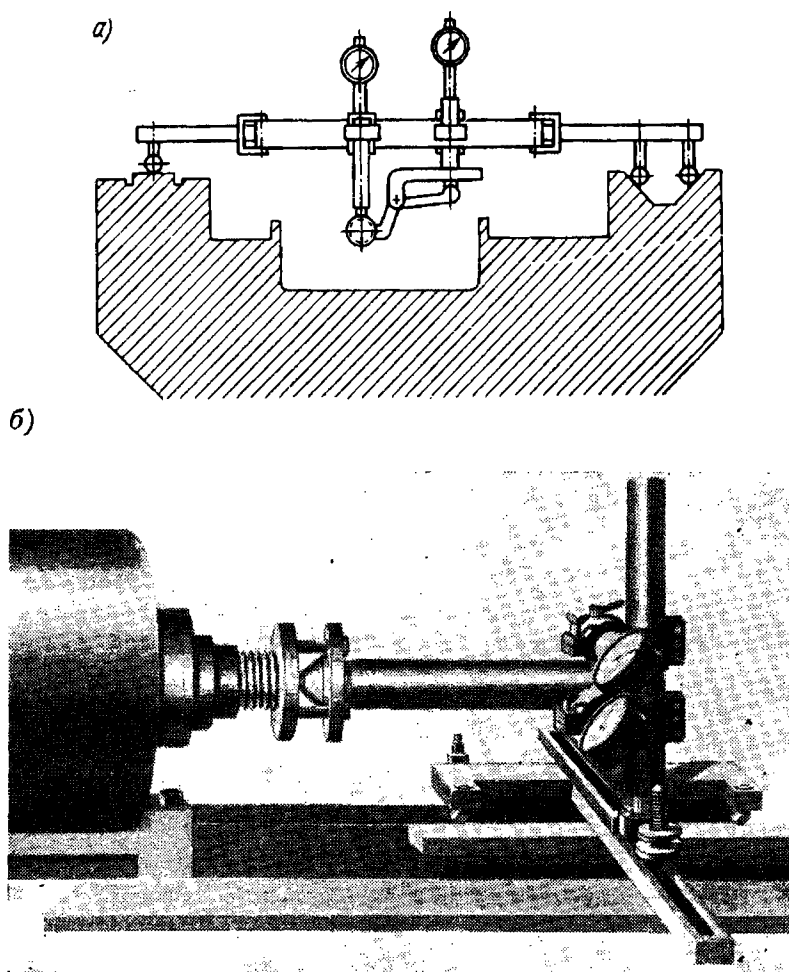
Примеры применения приспособления: *а* — схема проверки параллельности оси винта координаторосточного станка направляющим станины; *б* — проверка параллельности оси шпинделя направляющим станка
